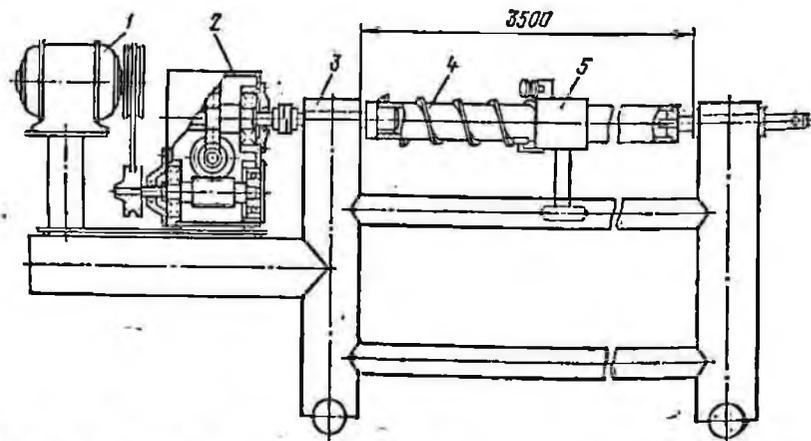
Устройство для сварки полых шнеков с использованием ручной электродуговой сварки:
